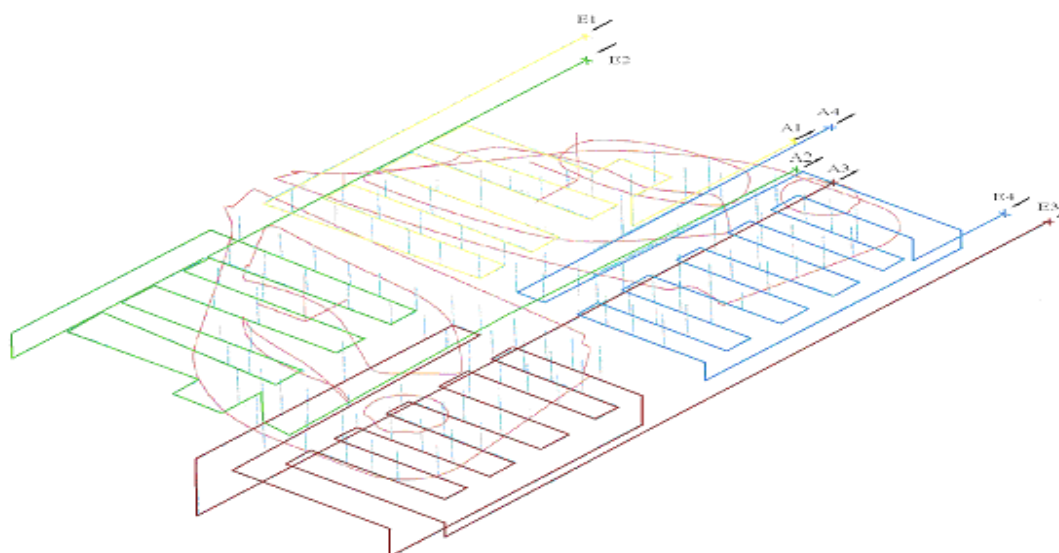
Tvárnice od firmy WFS-WERKZEUG UND FORMENBAU SCHMIDT GmbH.
